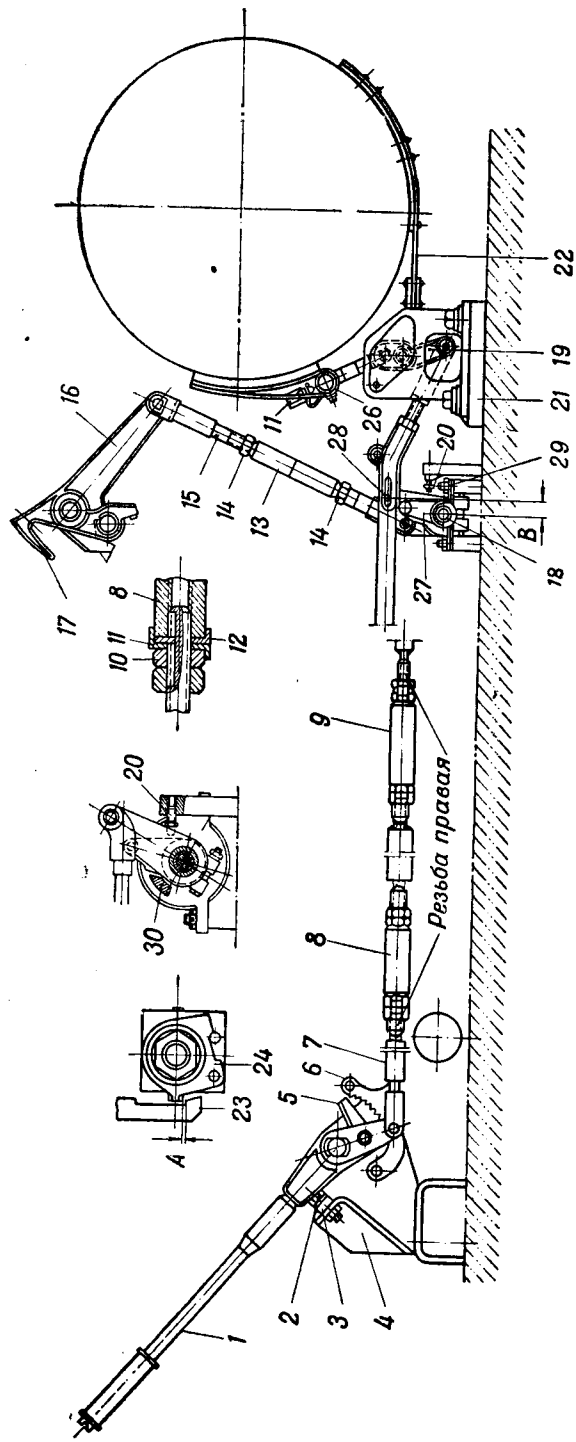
Привод управления механизмом поворота и остановочными тормозами:
